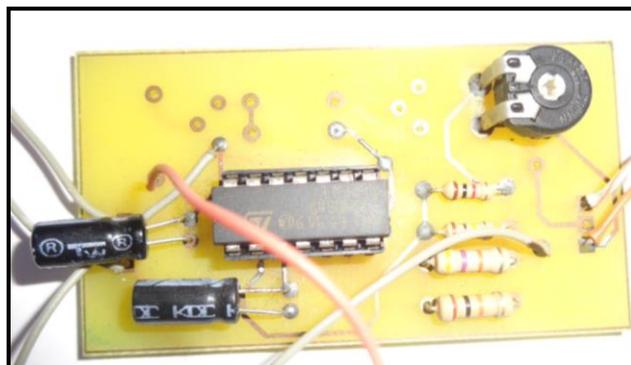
Diseño del PCB para el circuito acondicionador de señal
